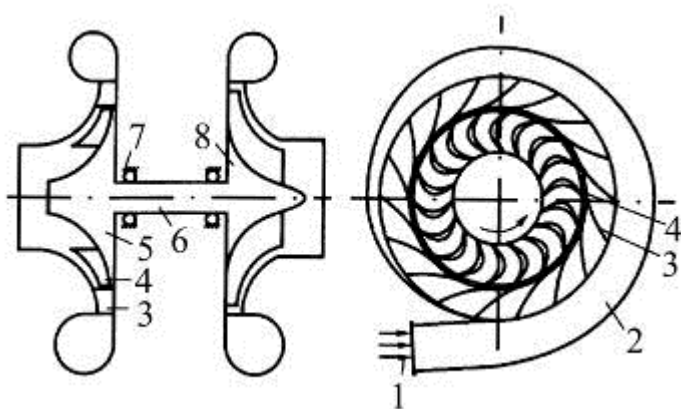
Принципиальная схема турбохолодильника: 1 - патрубок, 2 - улитка, 3 - сопловой аппарат, 4 - лопатки рабочего колеса, 5 - рабочее колесо турбины, 6 - вал, 7 - подшипник, 8 - рабочее колесо вентилятора
